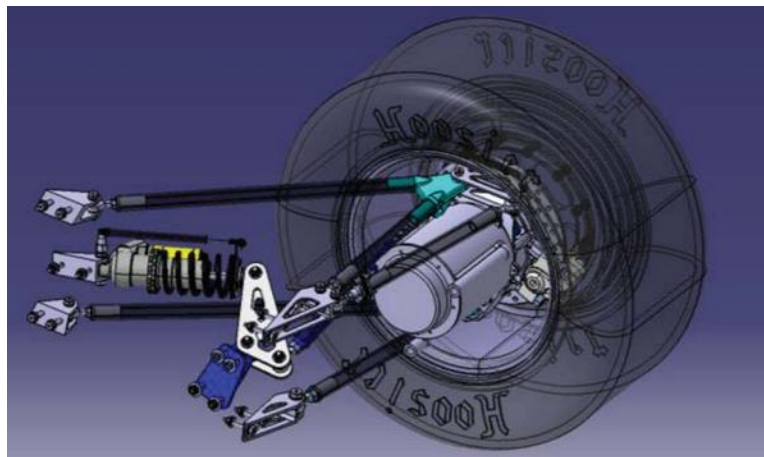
Ensamblaje del motor propuesto por Hu *et al.* [12] montado en el eje de la rueda.
